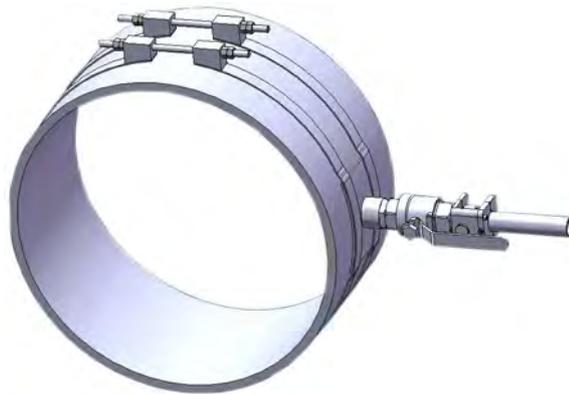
Exemple d'installation avec collier de prise en charge pour un diamètre extérieur de 400 mm à 600 mm
